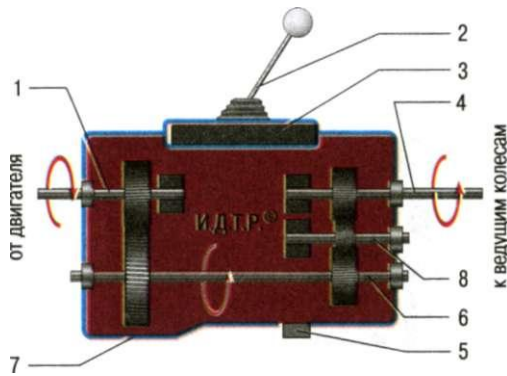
Схема работы коробки передач (передача заднего хода): 1 - первичный вал; 2 - рычаг переключения передач; 3 - механизм переключения передач; 4 - вторичный вал; 5 - сливная пробка; 6 - промежуточный вал; 7 - картер коробки передач; 8 - вал и шестерня заднего хода
